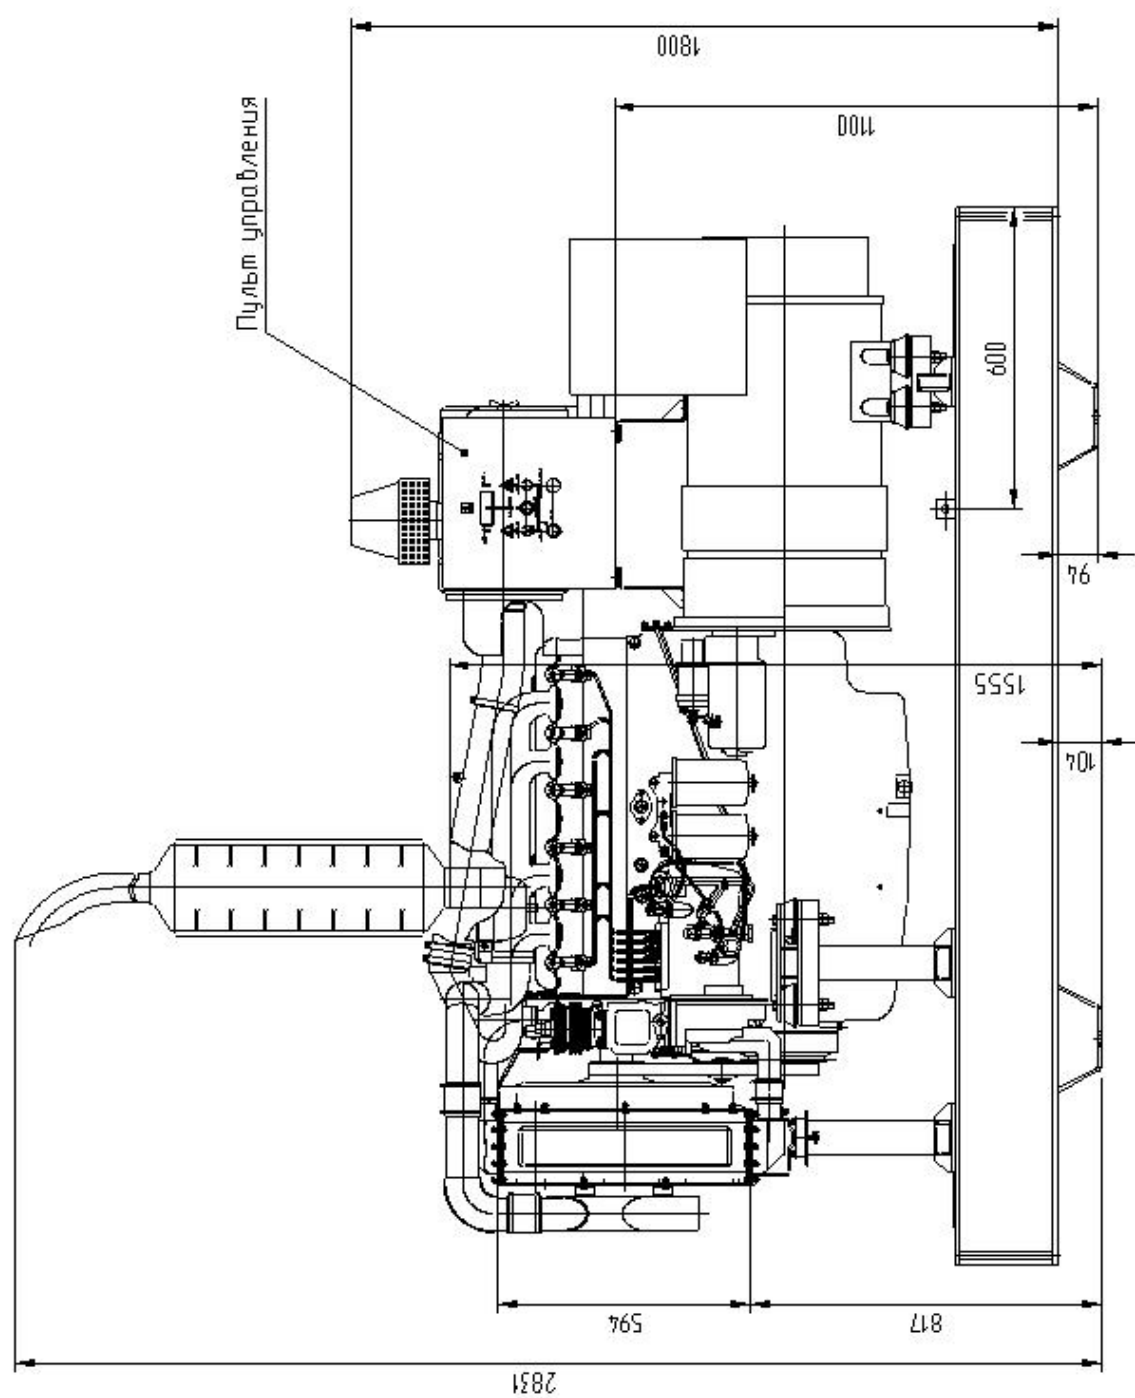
Монтажный чертеж установки ДГ-80/100/125/150 (вид сбоку).
